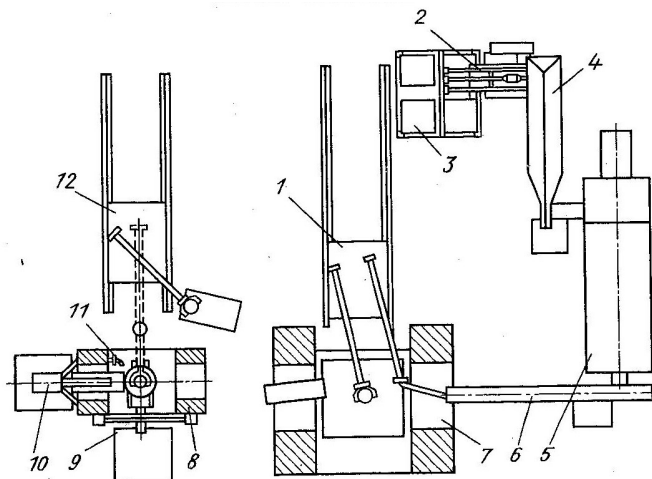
РТК на базі КГШП і обрізного пресу
